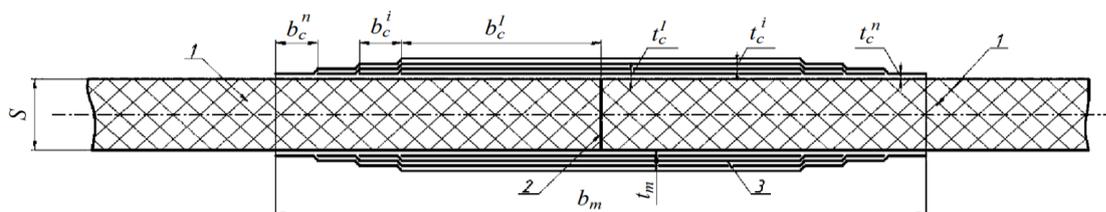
Конструктивна схема стикового (пазового) формованого з'єднання одношарових в'язей без оброблення кромки:
